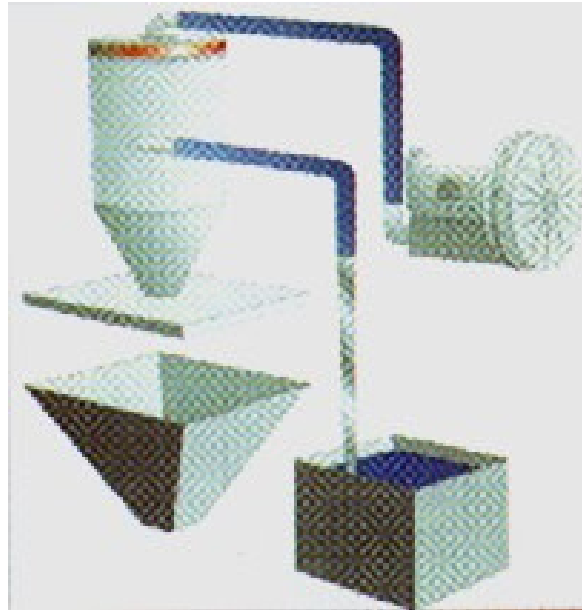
Um compressor aspira o ar de um funil, fazendo com que o mesmo seja alimentado com material de um silo, saco ou tambor. Quando o funil da máquina (em baixo) precisa ser alimentado, o funil do transportador abre e despeja seu conteúdo.
